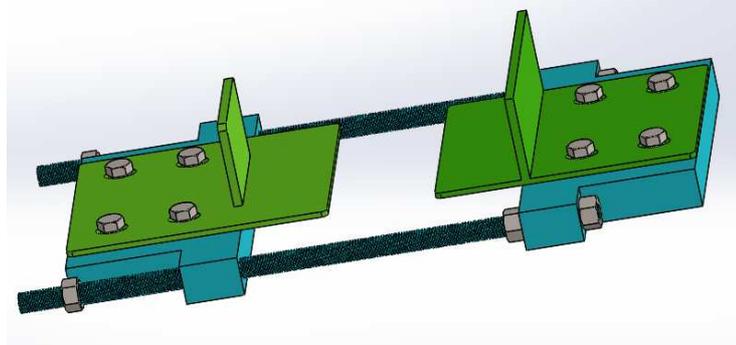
assemblage de la partie mobile avec la partie fixe
